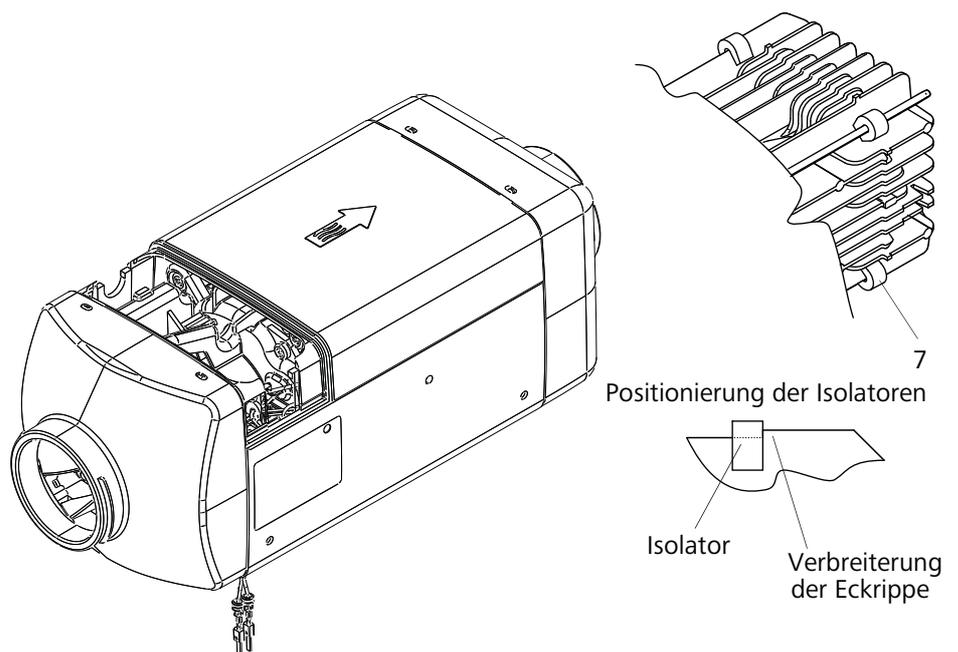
Entfernen / Aufsetzen der Gehäuseteile
